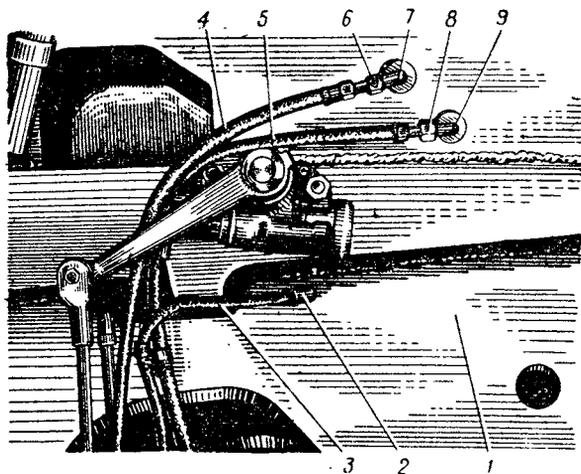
Присоединение гибких шлангов к корпусу машины:
